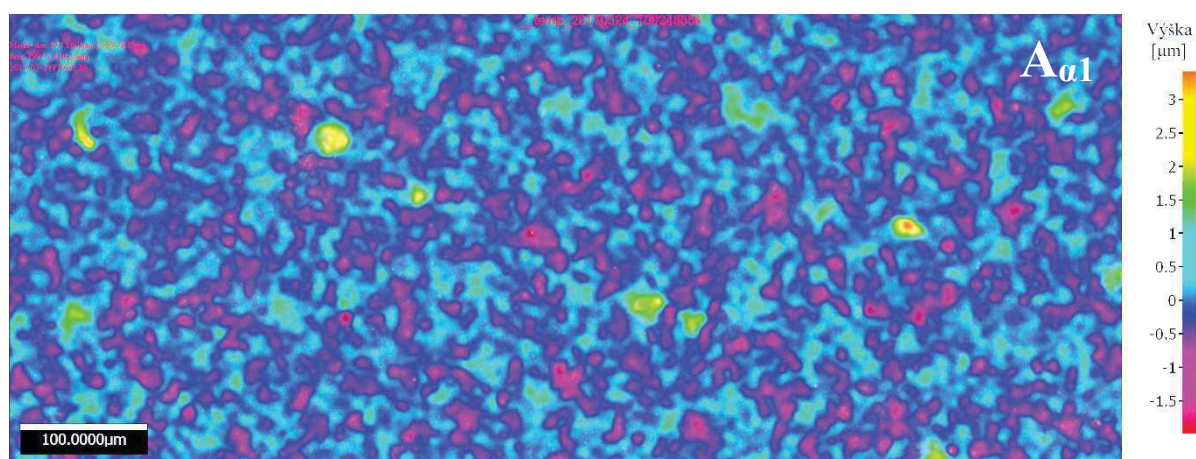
Povrch hřbetu ostřený technologií EDM-G zobrazený ve 3D.
